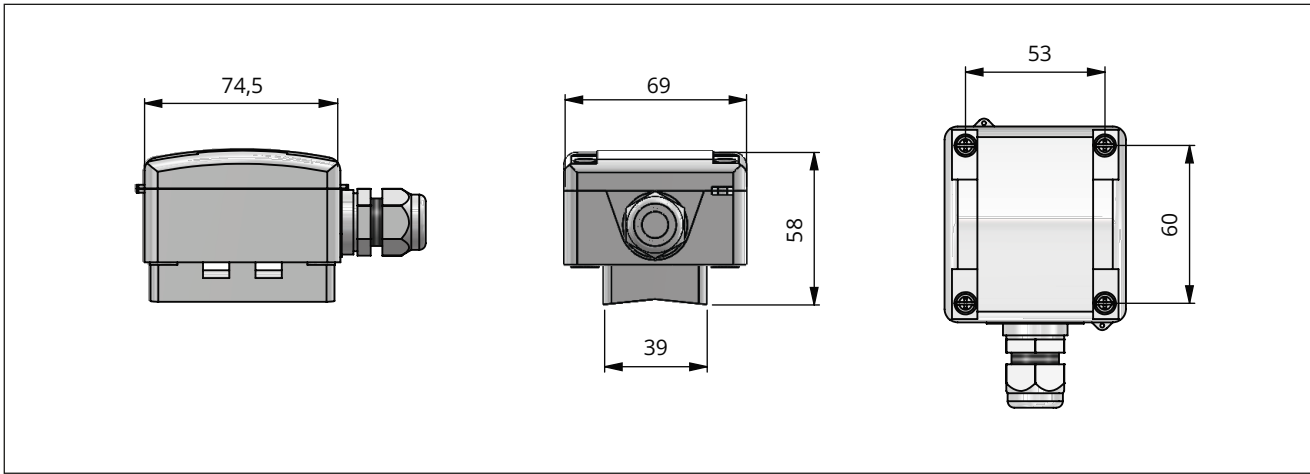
Maße in mm · Anlegesensor Typ 5267-3
